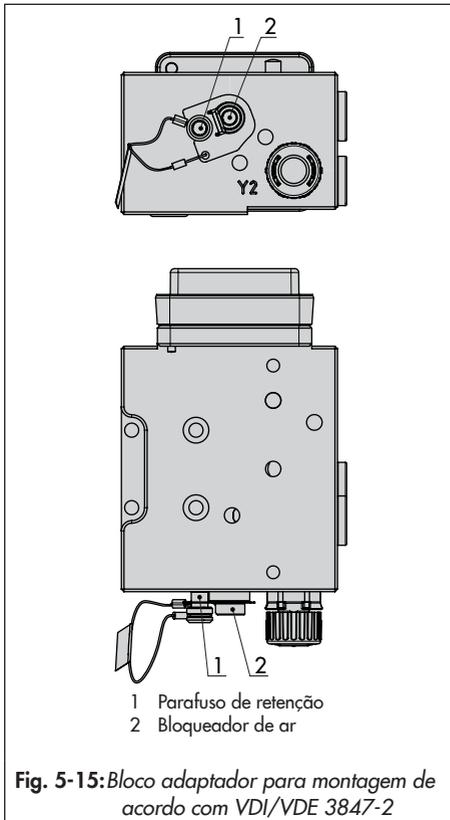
Bloco adaptador para montagem de acordo com VDI/VDE 3847-2
